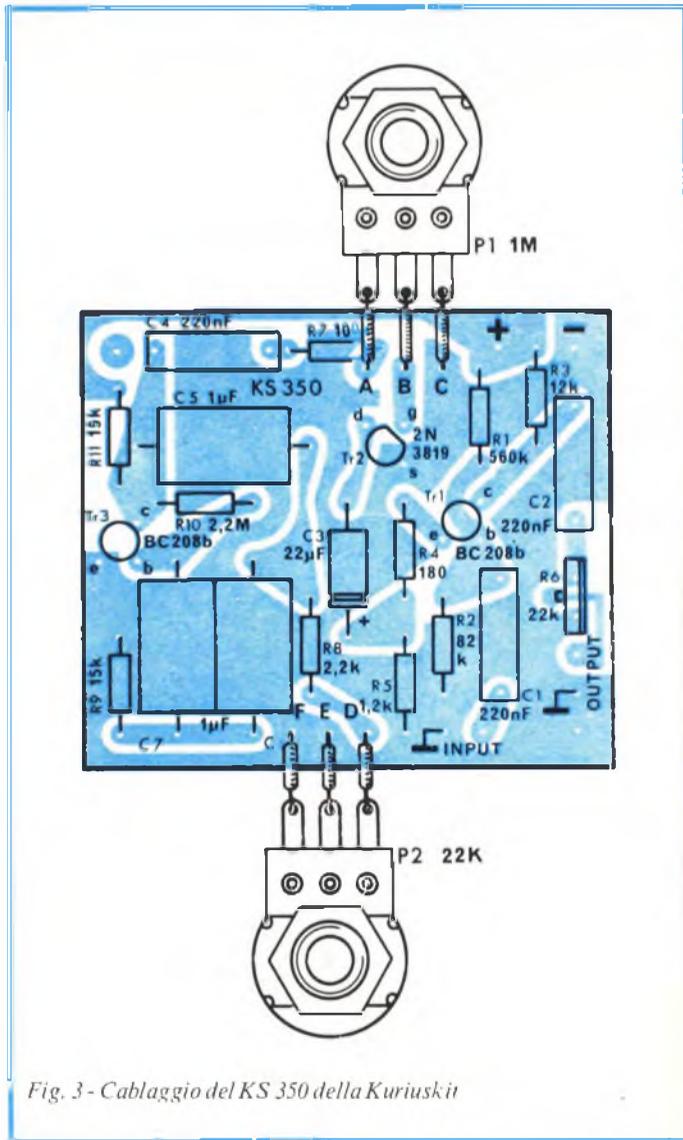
Cablaggio del KS 350 della Kuriuskit
